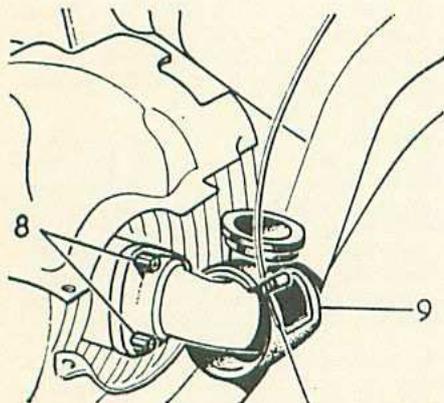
Prise de chauffage sur tubulure d'admission côté gauche.
